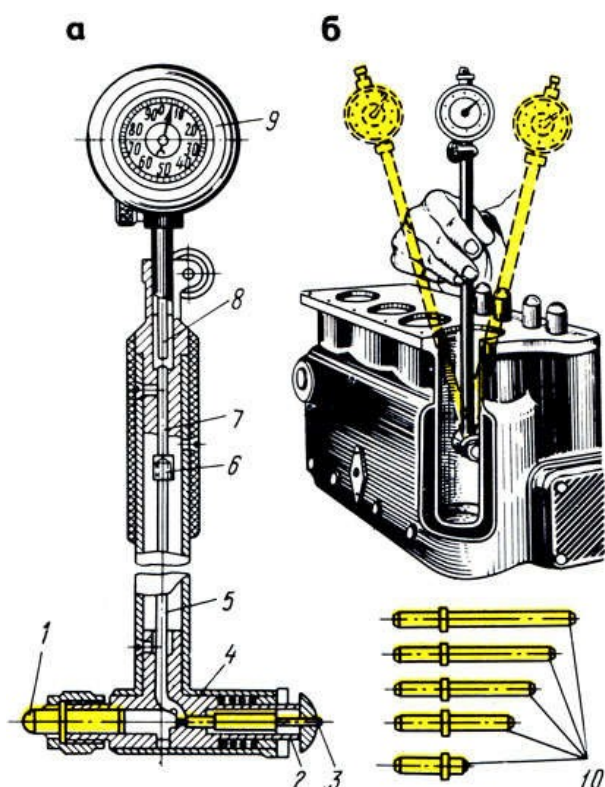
Индикаторный нутромер: а - устройстве, б - прием измерения; 1,3 - измерительные стержни, 2 - направляющая втулка, 4 - корпус, 5 - толкатель, 6 - шток, 7 - трубка, 8 - наконечник, 9 - индикатор, 10 - сменные стержни
